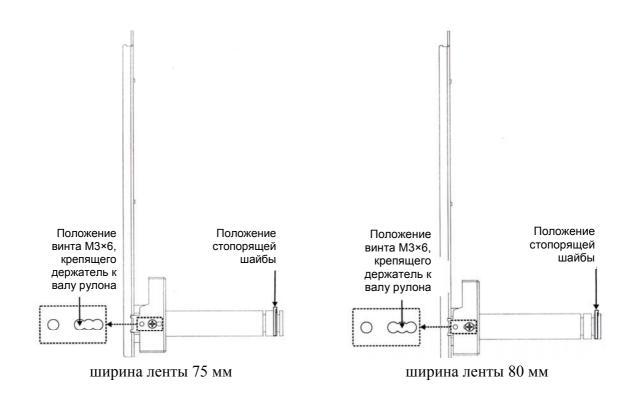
Элементы регулировки положения рулона ленты (вид рулонодержателя сверху)
